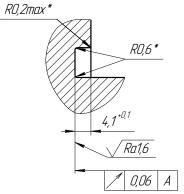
Эскиз торцевой канавки с низкой шероховатостью
